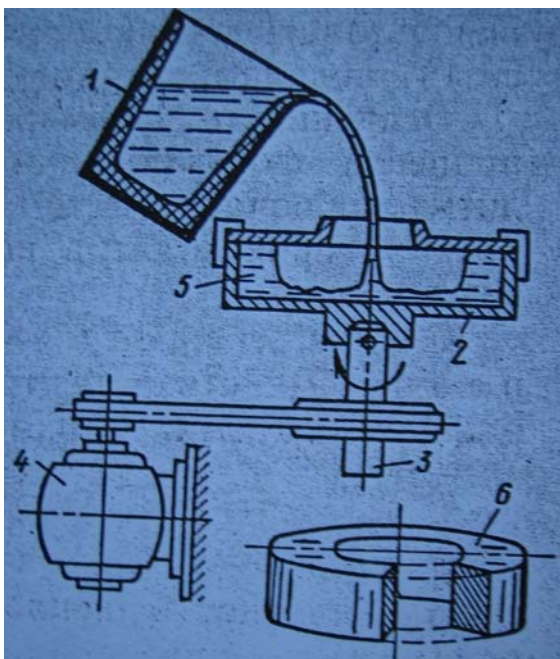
Схема получения отливки при вращении формы вокруг вертикальной оси: 1- ковш, 2- форма, 3- шпиндель, 4- электродвигатель, 5- расплав, 6- отливка.
